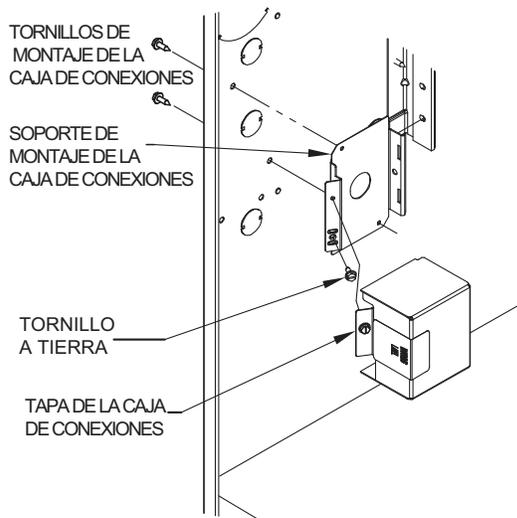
Desmontaje / Instalación de la caja de conexiones
